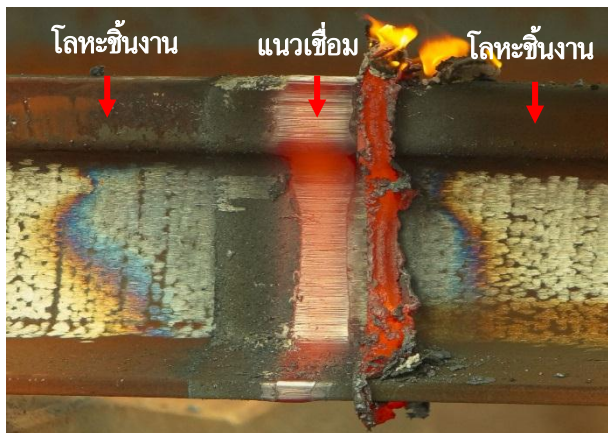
กรรมวิธีการเชื่อมด้วยความต้านทาน (Resistance upset welding)
